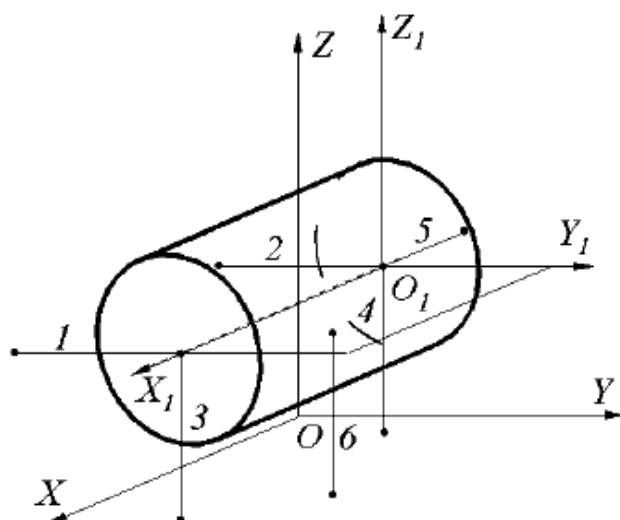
Наложение шести связей на цилиндрическую деталь
